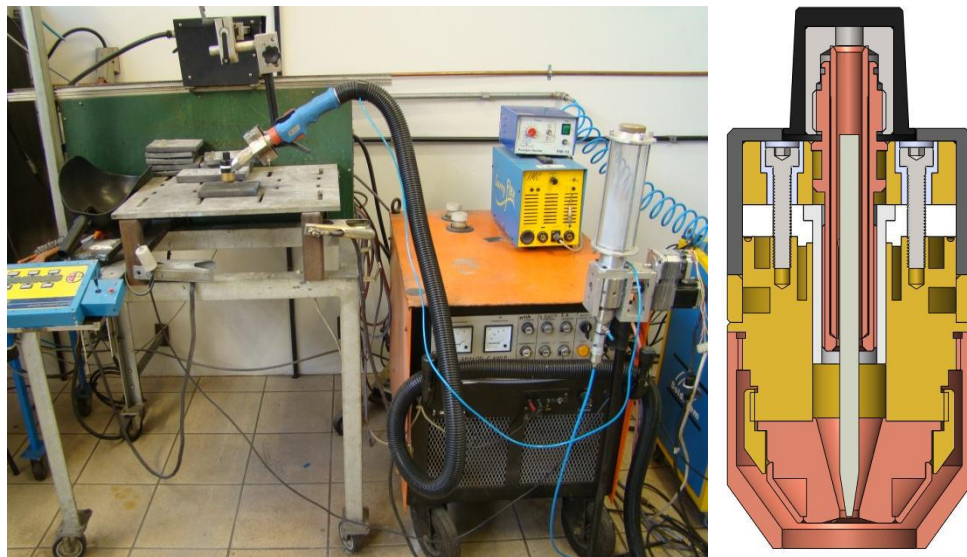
Bancada de trabalho Plasma com adição de pó e detalhe da tocha de soldagem.
